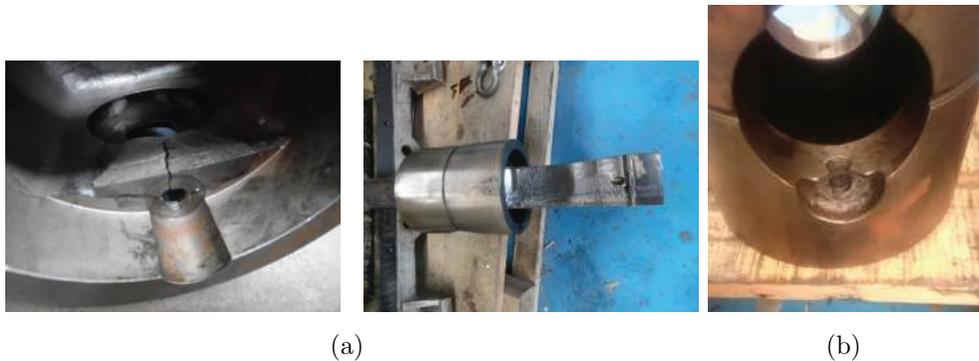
a) Inspección del Cross head No.1 fracturado. b). Inspección de Cross head No. 2 fracturado, mismo patrón de falla.
